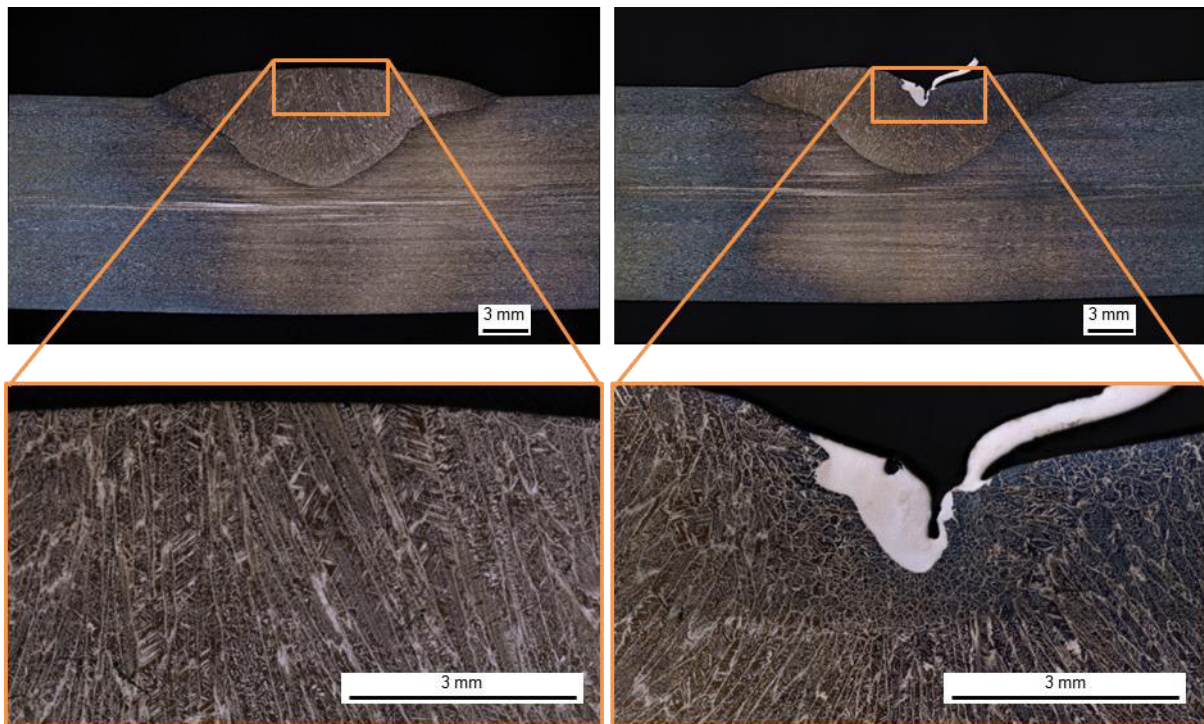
Makroschliffbilder einer Schweißraupe, links oben: Querschliff ohne eingebrachtes Thermoelement, links unten: Detailansicht der Gefügestruktur ohne eingebrachtes Thermoelement, rechts oben: Querschliff am eingebrachten Thermoelement, rechts unten: Detailansicht der Gefügestruktur am eingebrachtem Thermoelement
